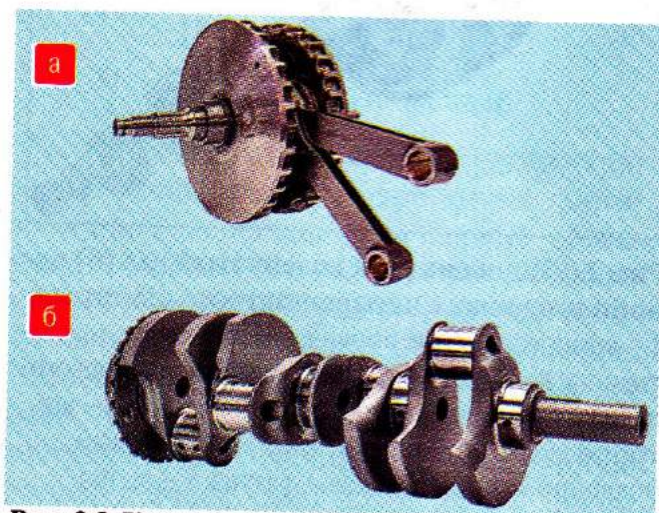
Шатуны: а – с неразъемной нижней головкой; б – с разъемной нижней головкой; 1 – шатун; 2 – сепаратор подшипника нижней головки шатуна и ролики; 3 – шатунная шейка (запрессована в щеки коленчатого вала); 4 – крышка шатуна; 5 – вкладыши; 6 – шатунные болты
